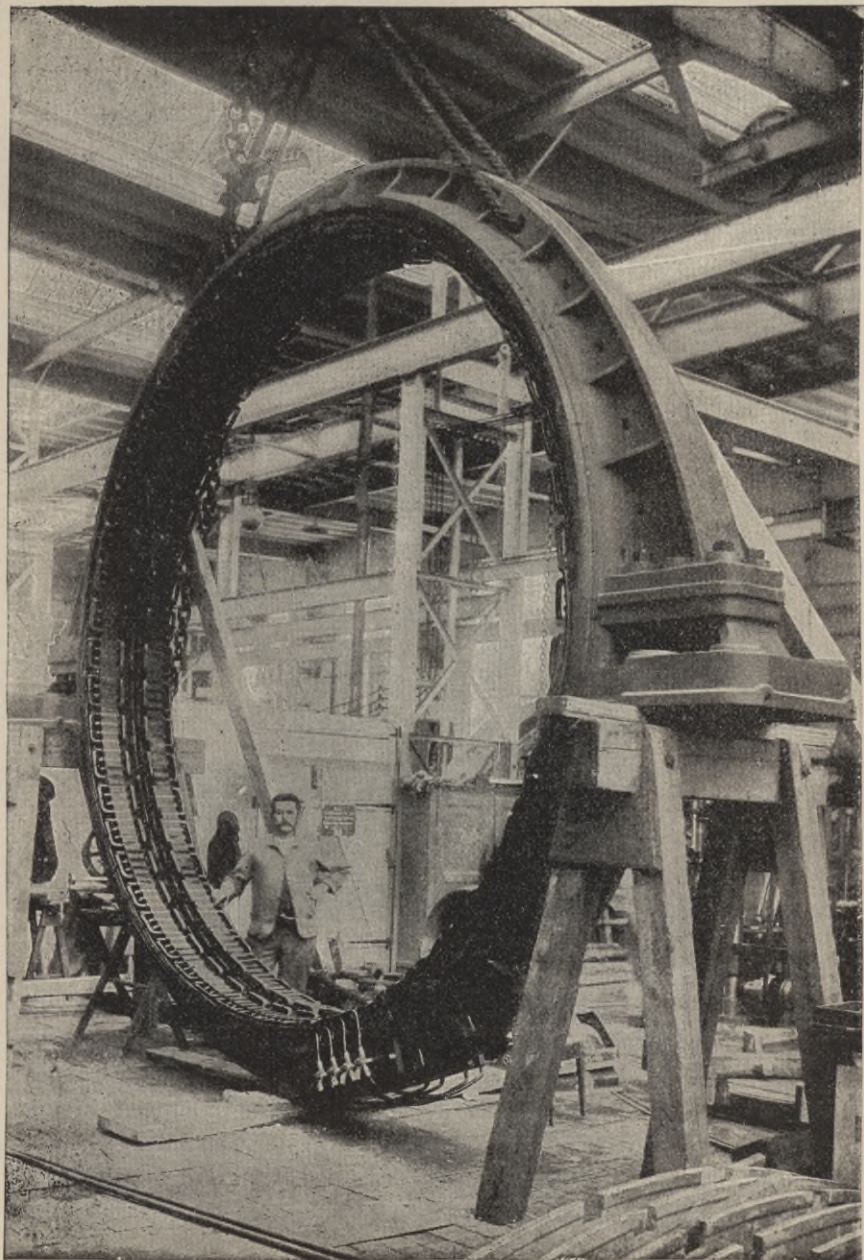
Doppelanker einer langsam laufenden Inductormachine.
